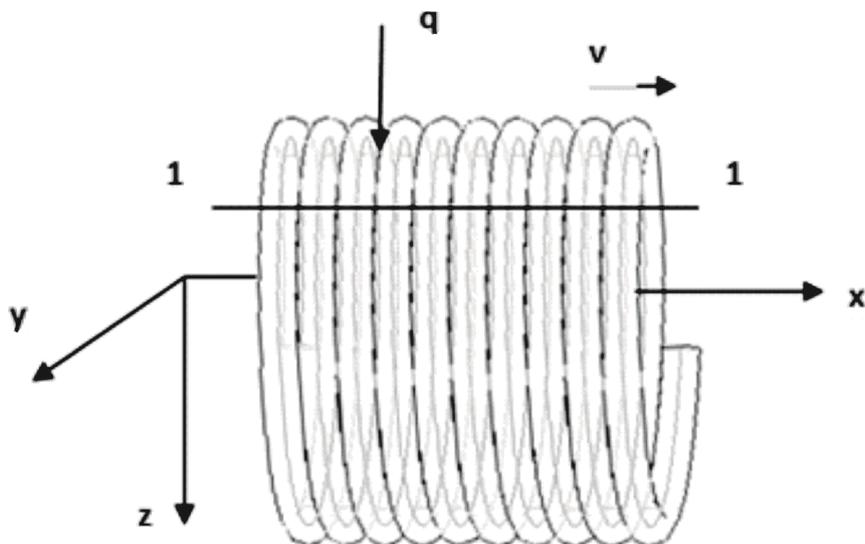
Схема лазерной сварки витков пружинно-витого канала
